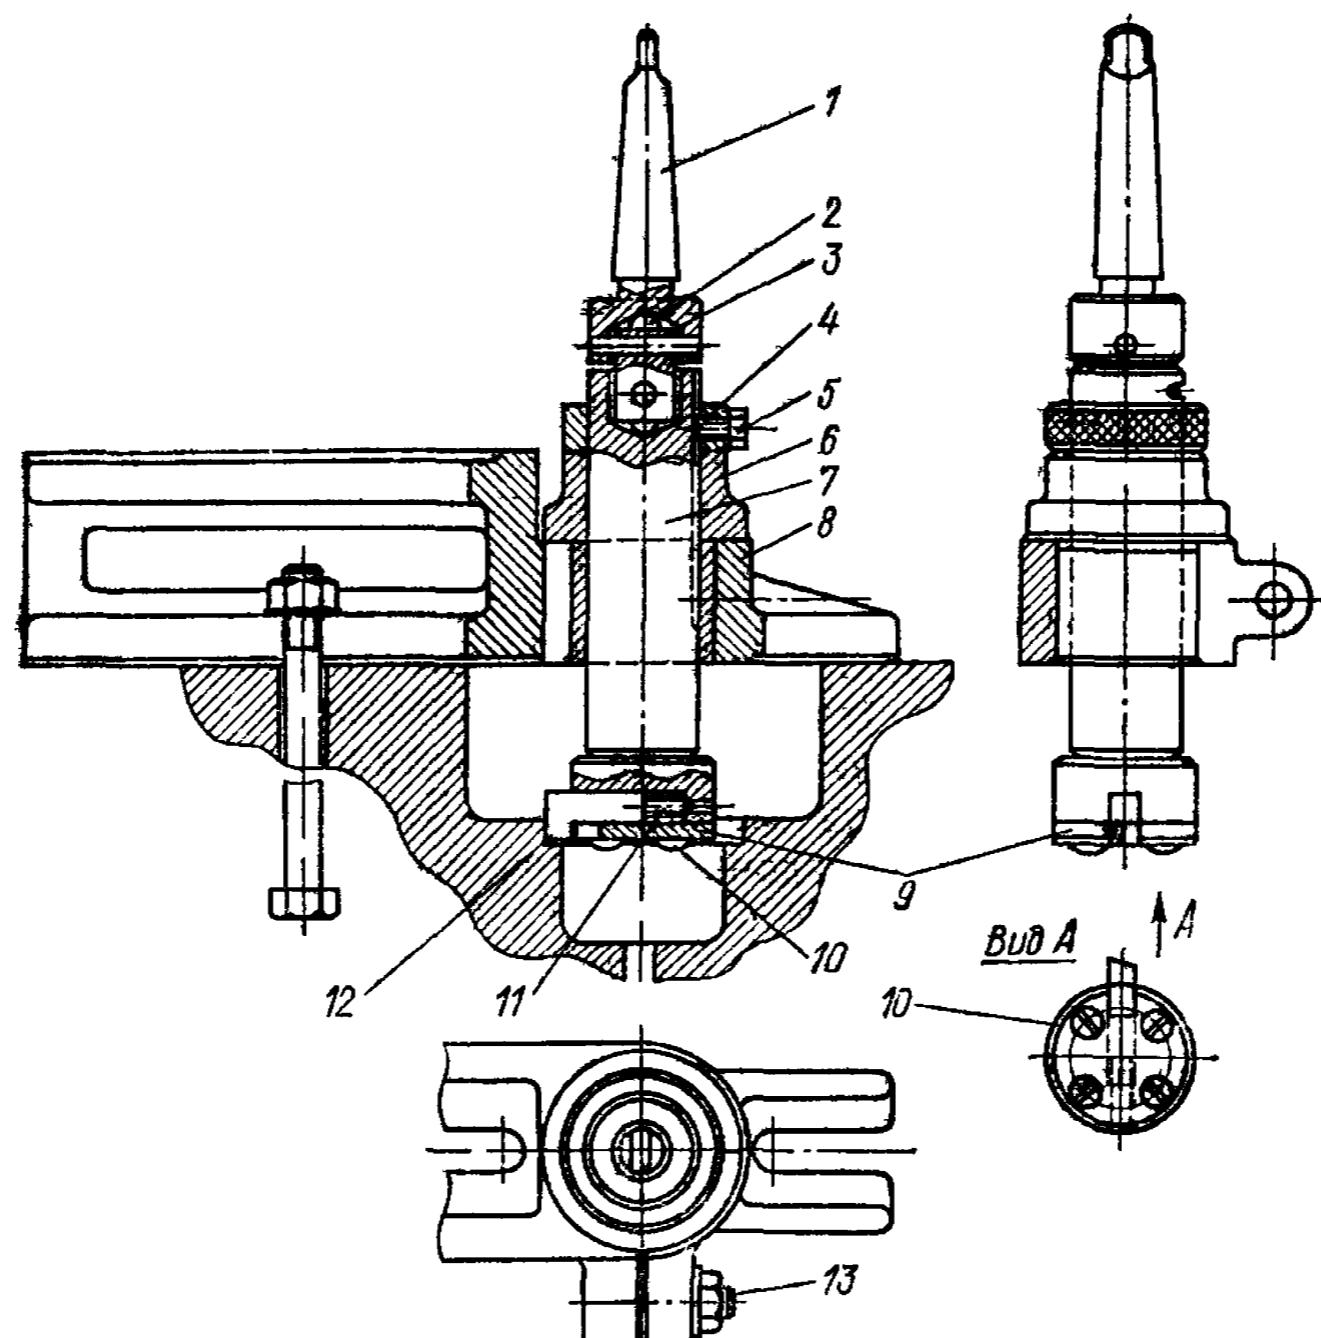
Приспособление для растачивания гнезда седла клапана:
